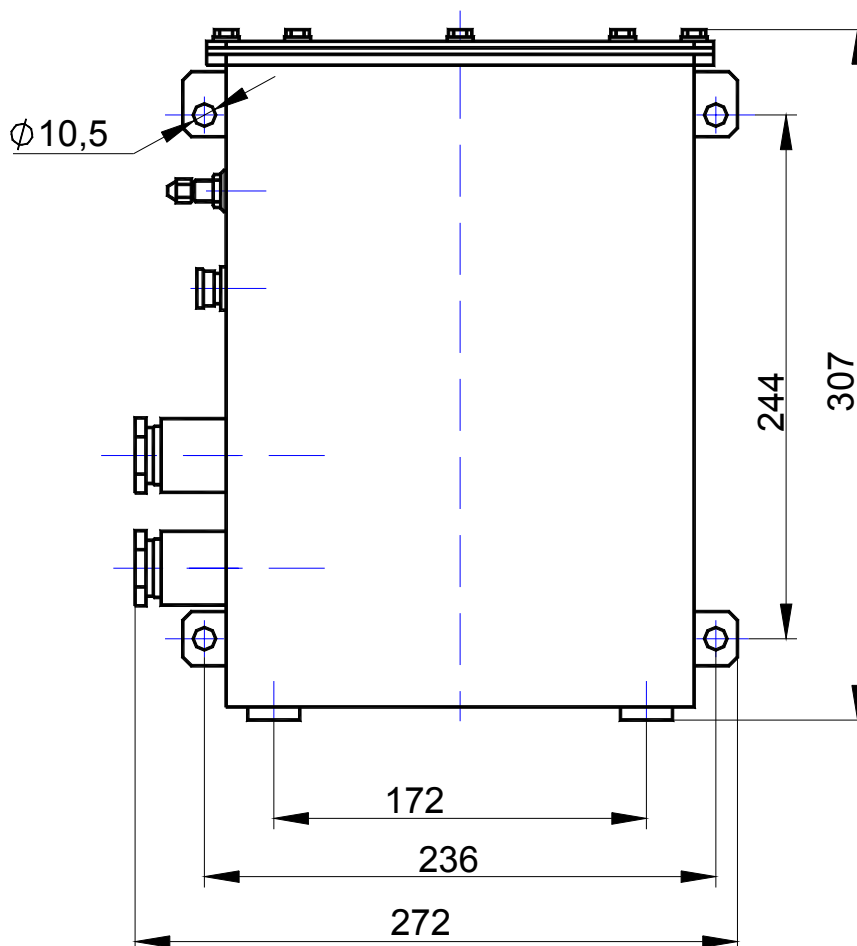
Регенератор в герметичном корпусе, вид спереди
